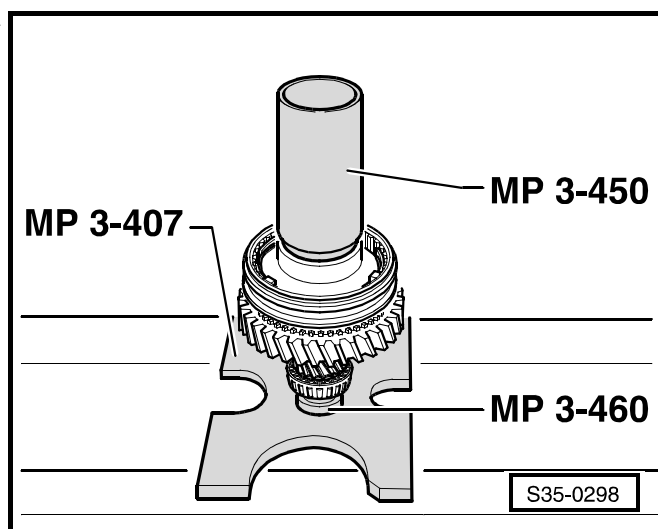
Положение для сборки наружного кольца для 1-ой и, соотв., 3. 3-ей передач
